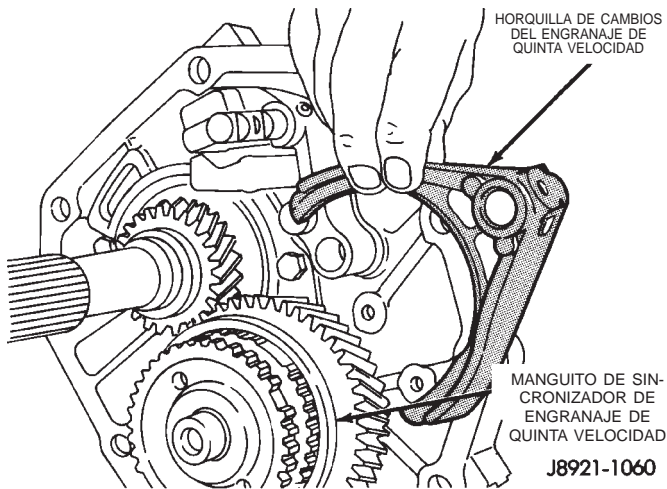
Instalación de horquilla de cambio del engranaje de quinta velocidad
